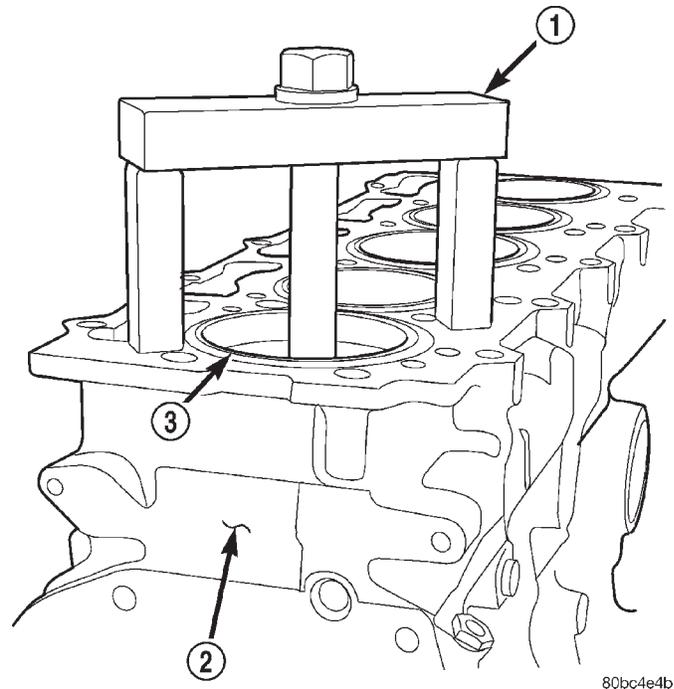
Ausbauwerkzeug/Zylinderlaufbuchsen
